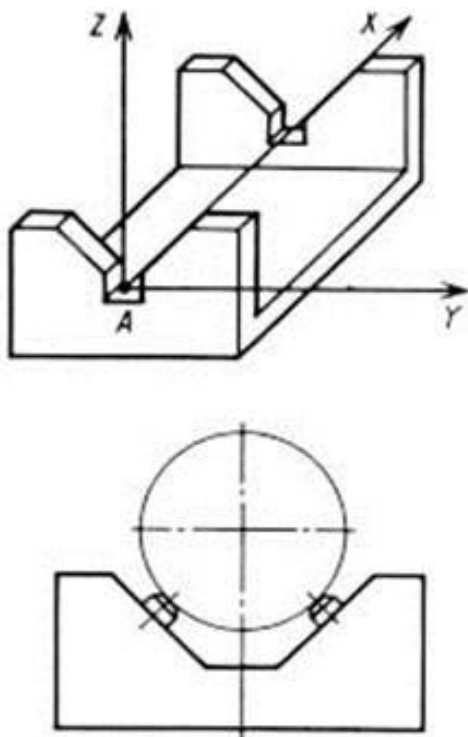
Призма для установки цилиндрических заготовок большой длины по «черным» (необработанным) поверхностям.
